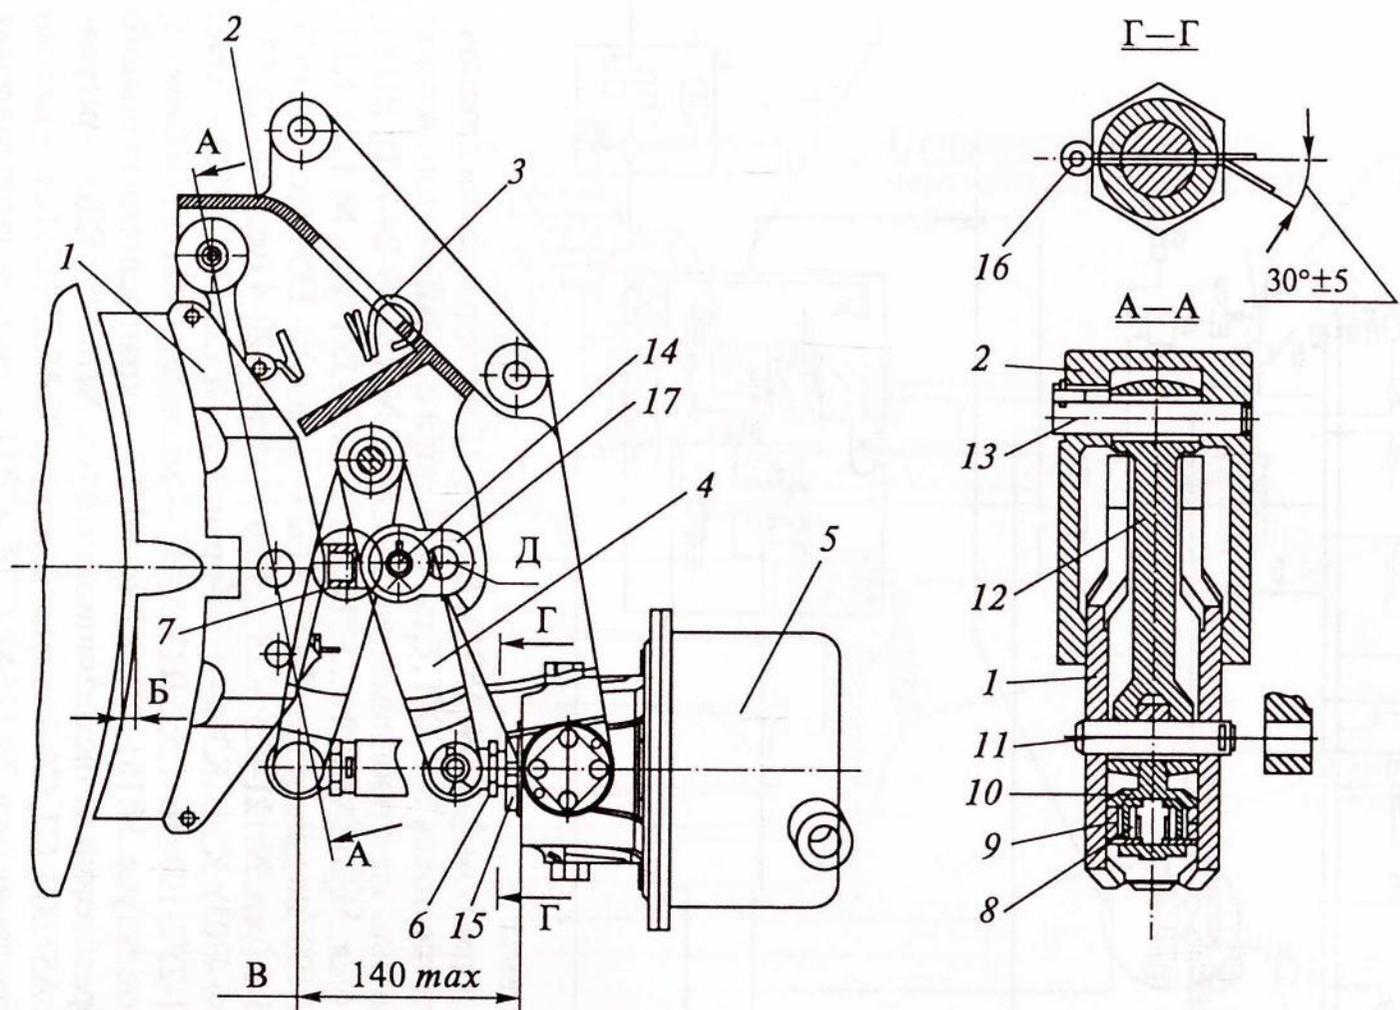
Тормоз колодочный с пневмоприводом:
